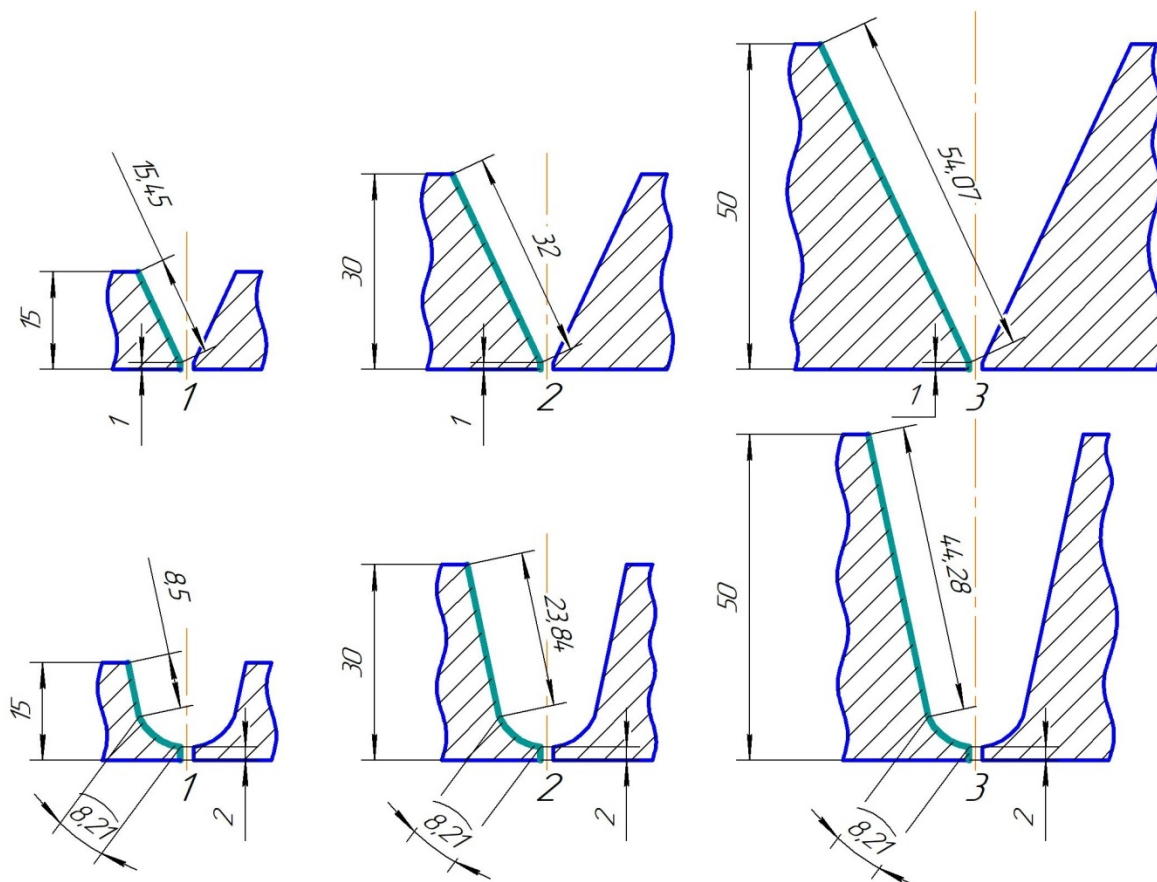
Расчет периметра сварочной ванны для двух способов
